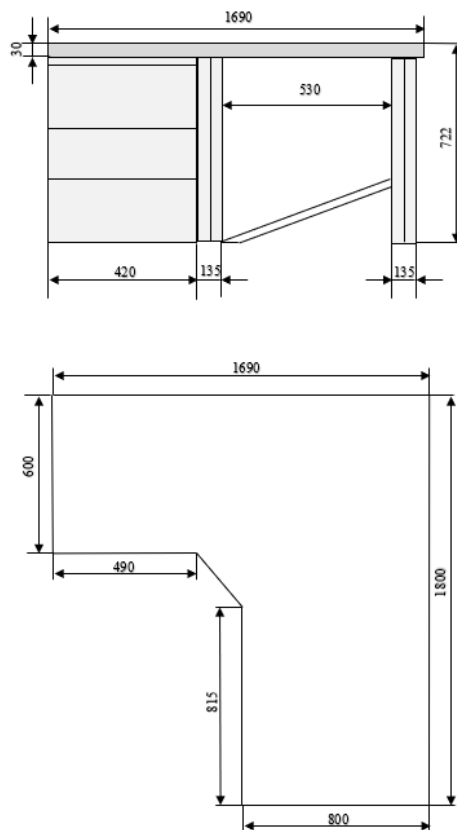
Croquis puesto de trabajo trabajador 1. Fuente: elaboración propia
